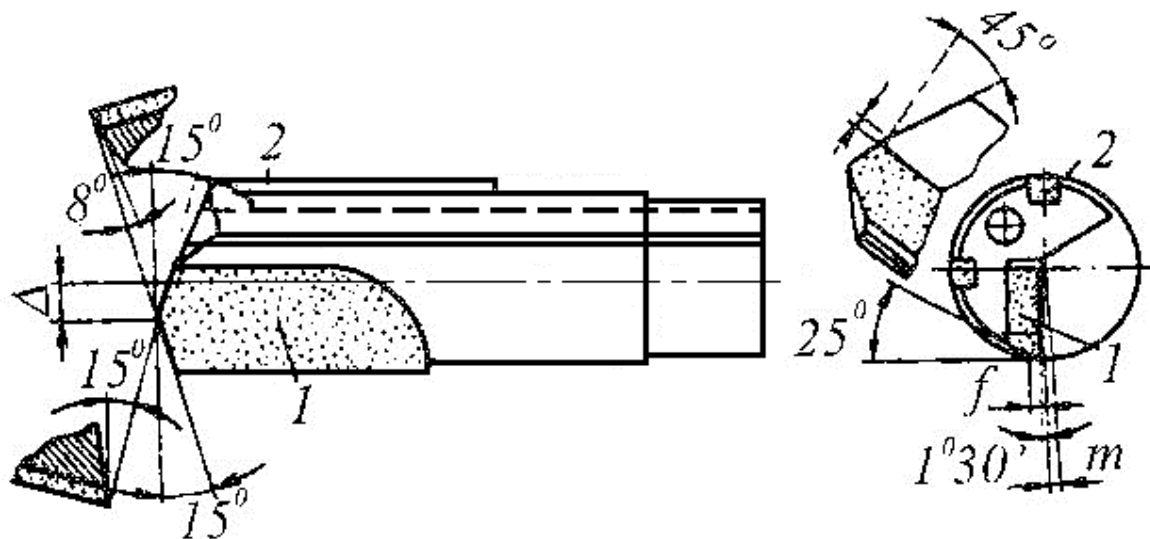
Свердло рушничне з припаяною пластинкою з твердого сплаву
